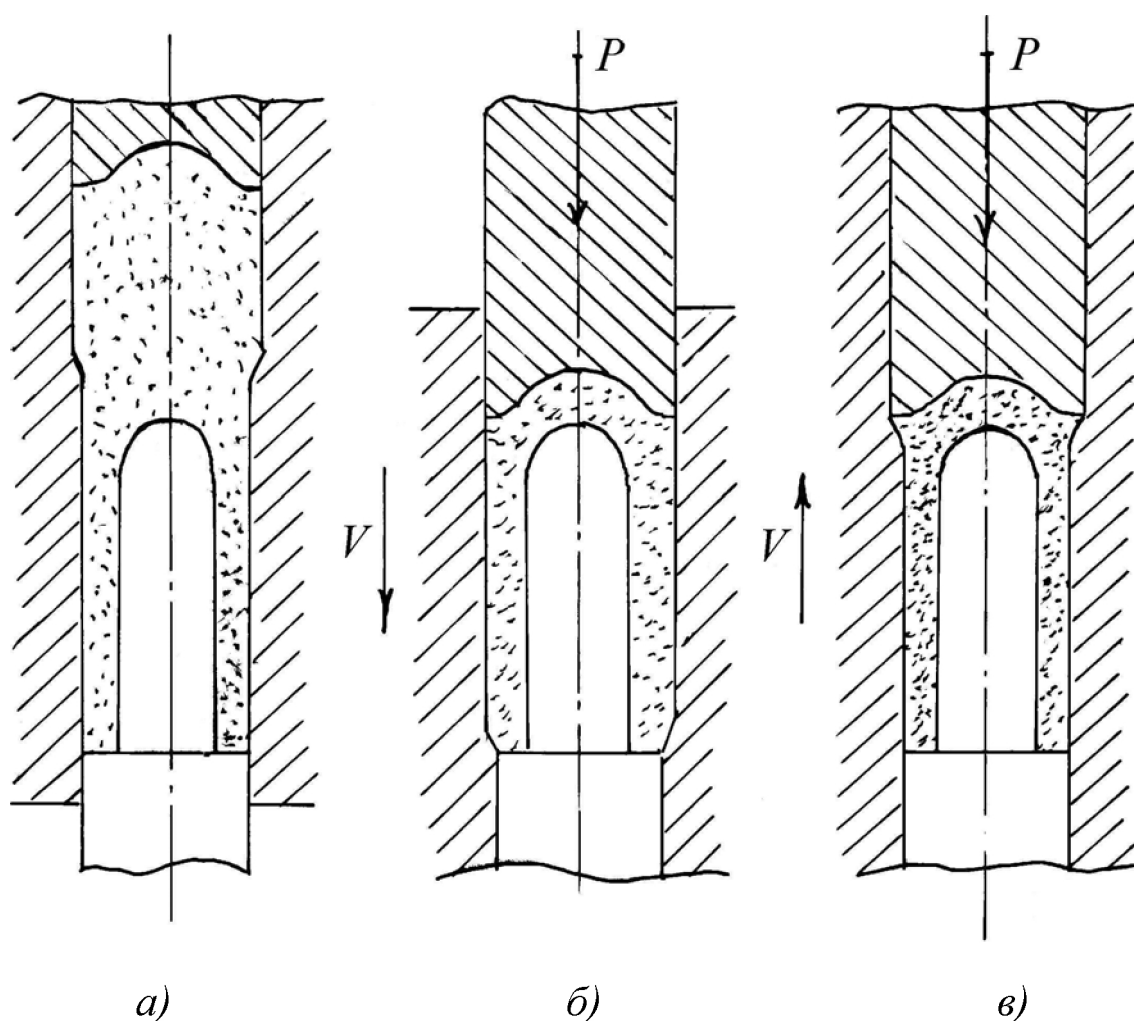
Схема формования стаканов с созданием интенсивных сдвигов в материале порошковой заготовки
